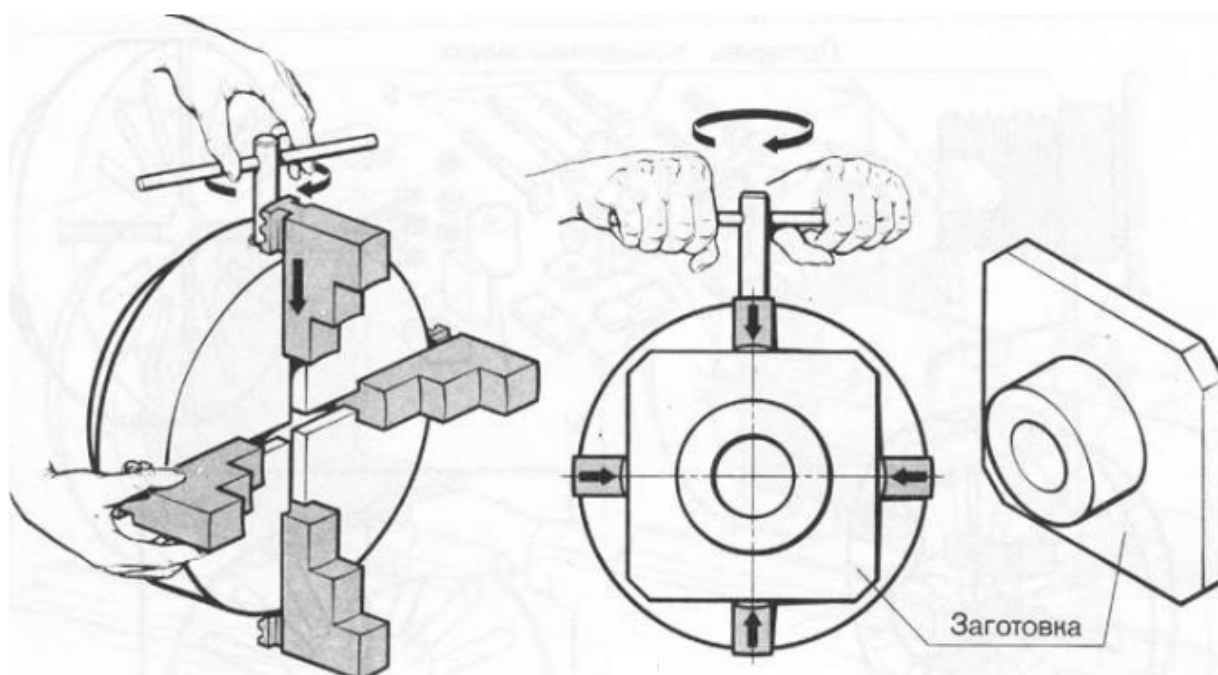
Установка заготовки в чотирьохкулачковому патроні
